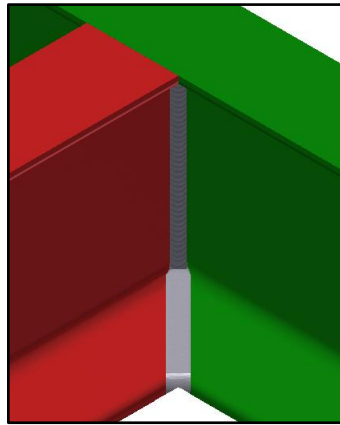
2 Detalle de Soldadura entre dos vigas transversal
